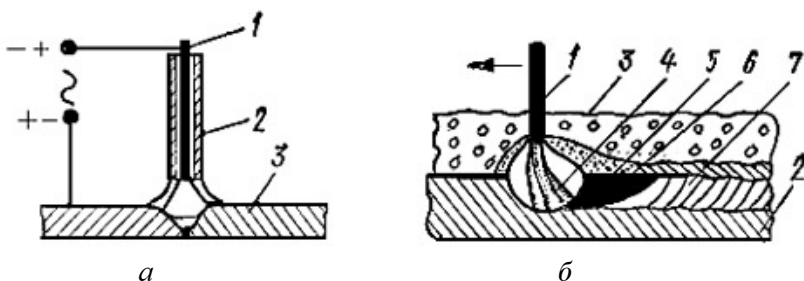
Сварка покрытым электродом (а): 1 – стержень, 2 – обмазка, 3 – основной металл; (б) автоматическая сварка под флюсом, направление сварки показано стрелкой: 1 – электродная проволока; 2 – основной металл, 3 – сварочный флюс, 4 – дуга, 5 – сварочная ванна, 6 – расплавленный флюс, 7 – расплавленный металл. Столб дуги со всех сторон окружен слоем флюса толщиной 30...50 мм
